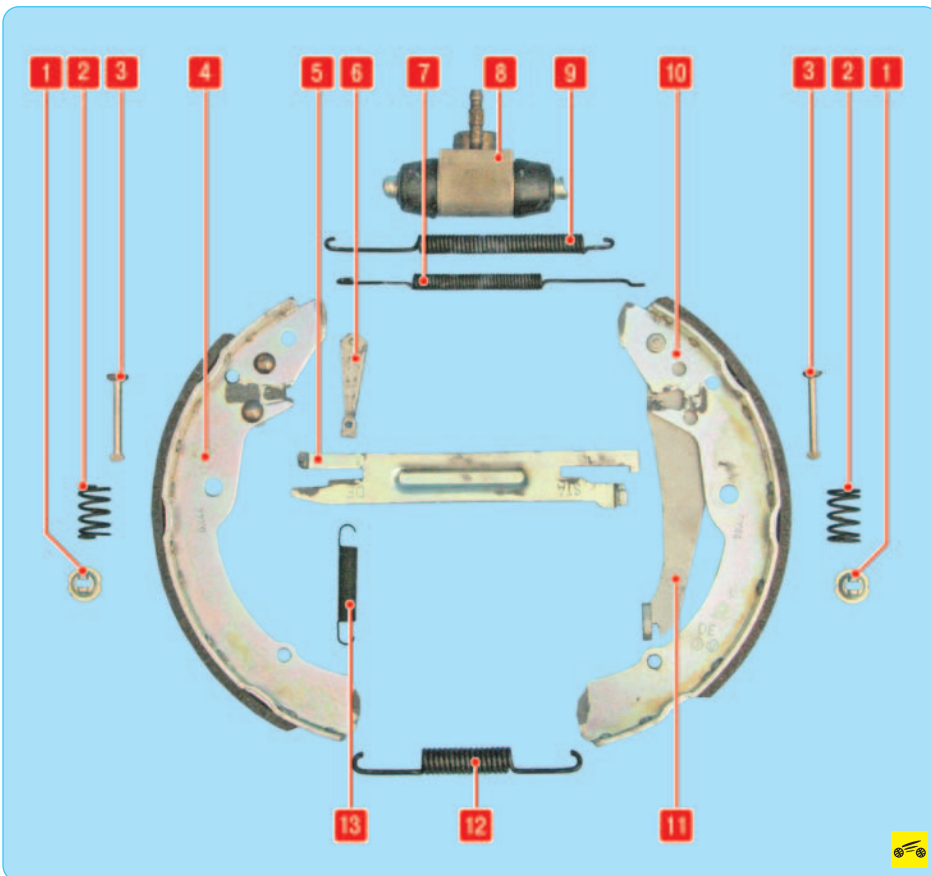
Детали тормозного механизма заднего колеса барабанного типа (показаны детали тормозного механизма с левой стороны): 1 – чашка прижимной пружины; 2 – прижимная пружина; 3 – опорная стойка тормозной колодки; 4 – передняя тормозная колодка; 5 – распорная планка; 6 – клин механизма регулировки зазора; 7 – верхняя стяжная пружина; 8 – рабочий цилиндр; 9 – оттяжная пружина распорной планки; 10 – задняя тормозная колодка; 11 – разжимной рычаг привода стояночного тормоза; 12 – нижняя стяжная пружина; 13 – пружина механизма регулировки зазора
